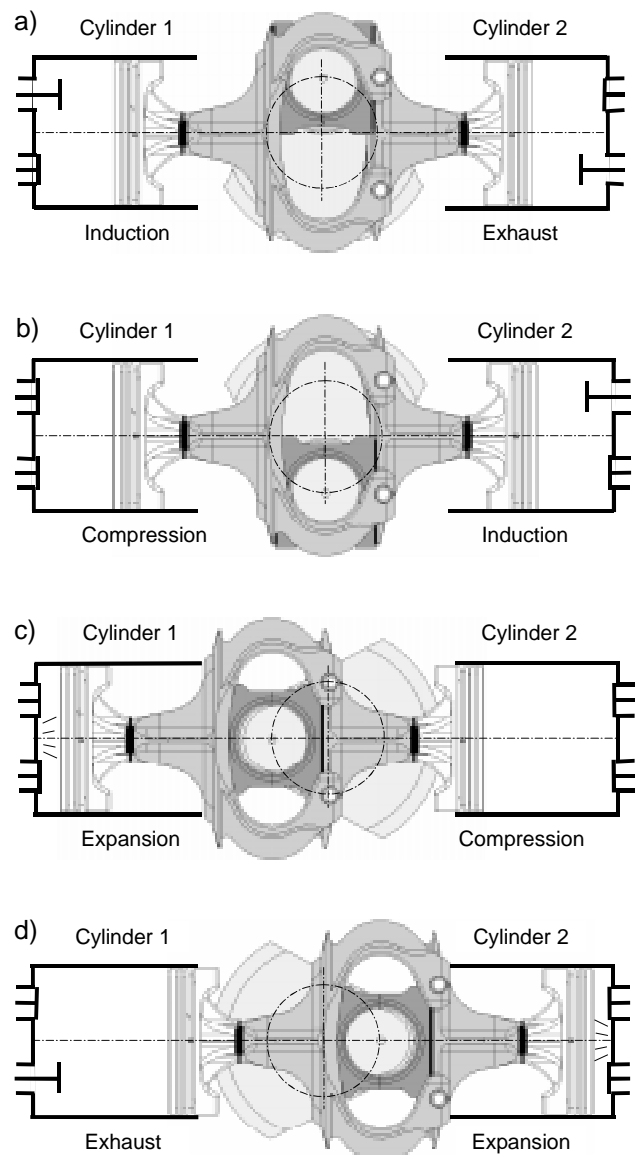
Arbeitszyklus /2/; a) 90° KW, b) 270° KW, c) 360° KW, d) 540° KW
